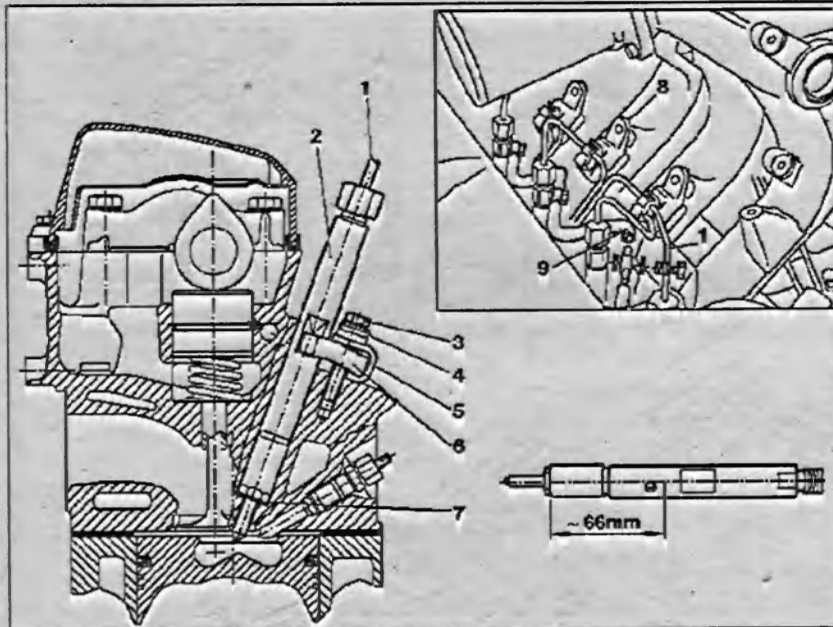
Снятие и установка держателя форсунки (двигатель 602.980):
